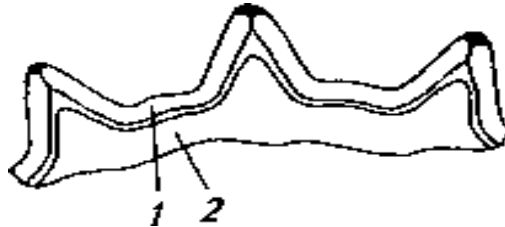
Схема відновлення ведучого колеса приваркою накладок:
